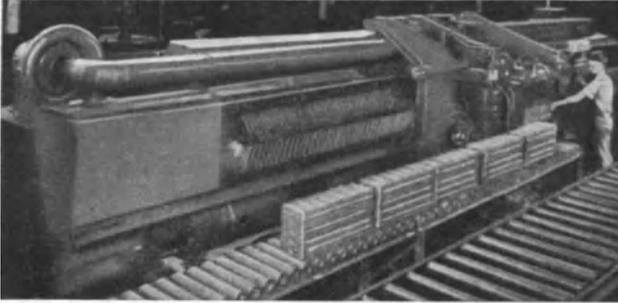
Sonderräummaschine für Zylinderblockbearbeitung mit schwenkbarer Werkstückaufnahme.
